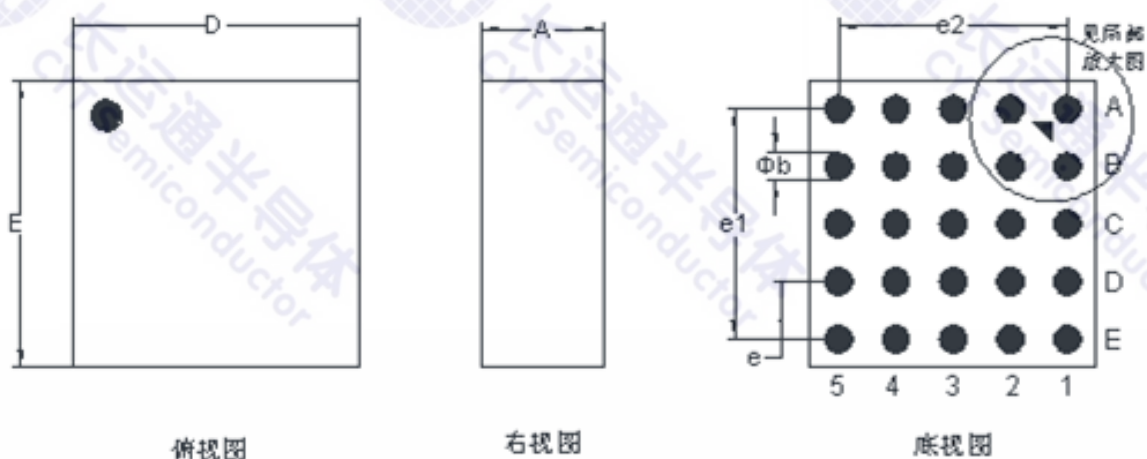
外形尺寸图(6.25mm×6.25mm×1.82mm LGA25)
